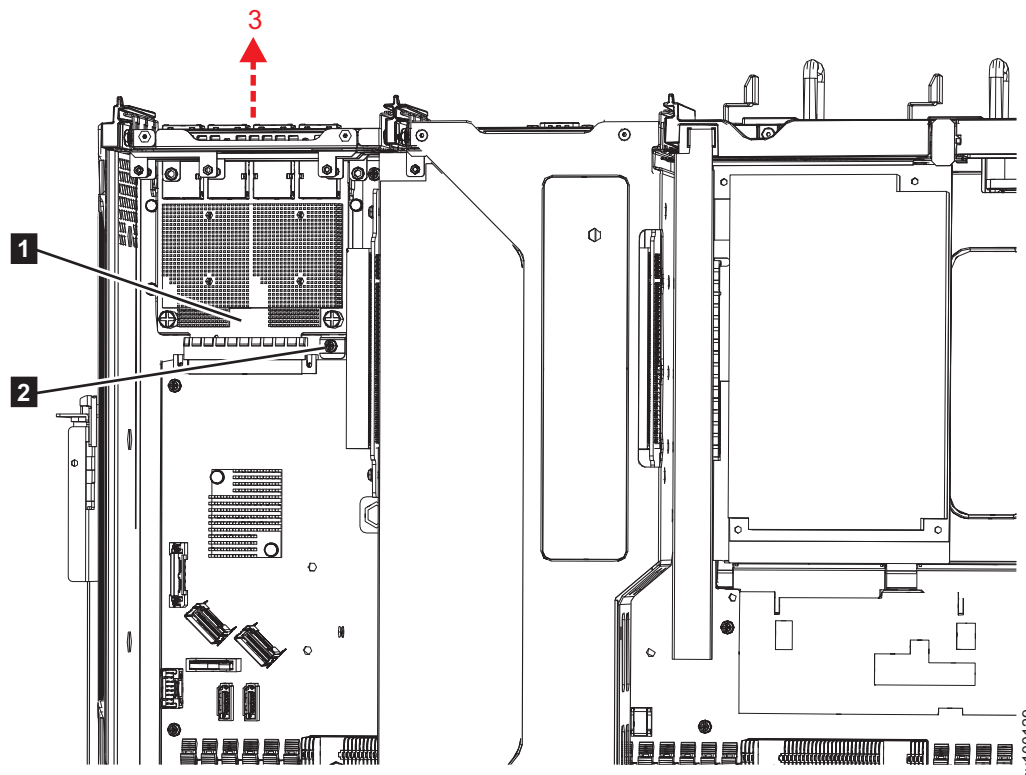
Removendo a placa de borda Ethernet do 2145-SV1
